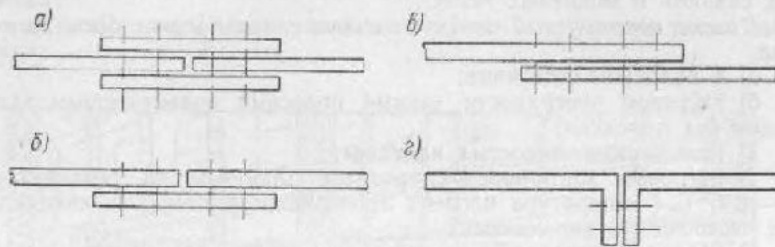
Конструкции соединений детали из пластмасс: а — с двумя накладными планками; б — с одной накладной планкой; в — внахлестку (внакрой); г — угловое соединение.
